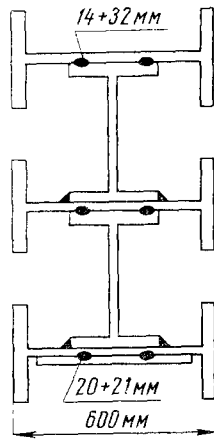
Поперечное сечение колонны, сваренной точечной сваркой
